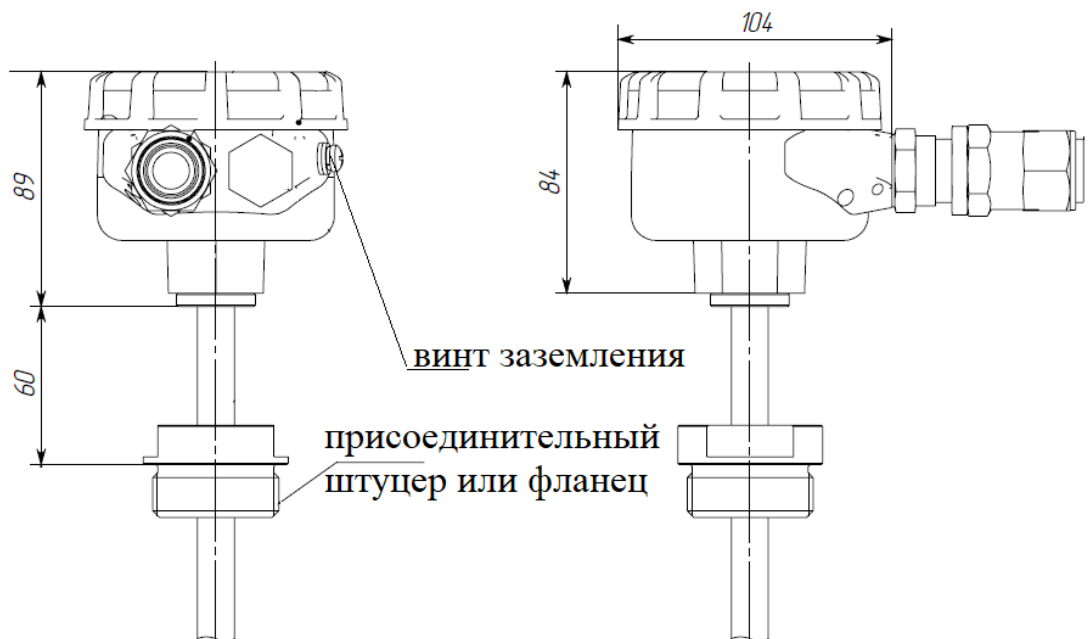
Габаритные размеры сигнализатора с корпусом А100, Н100
